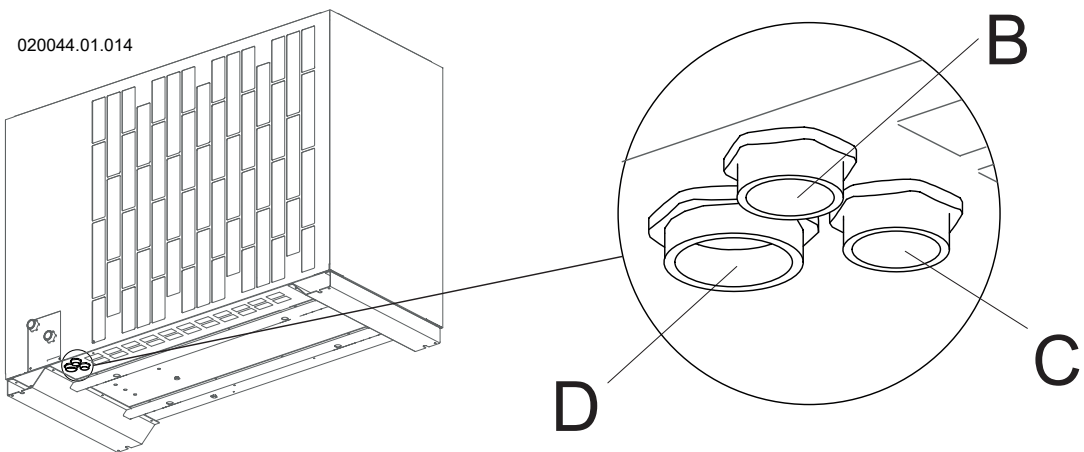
Posizione ingresso cavi per alimentazione, altri collegamenti elettrici e cavi di segnale
